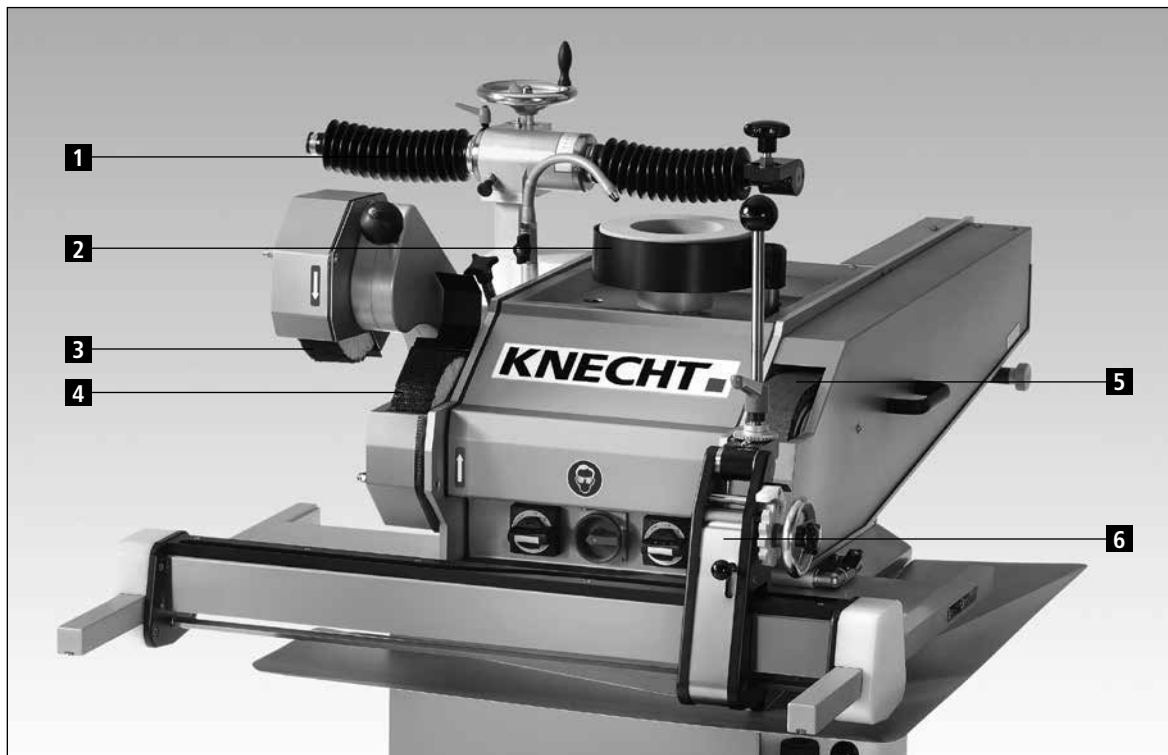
Vue d'ensemble de l'affûteuse S 20
